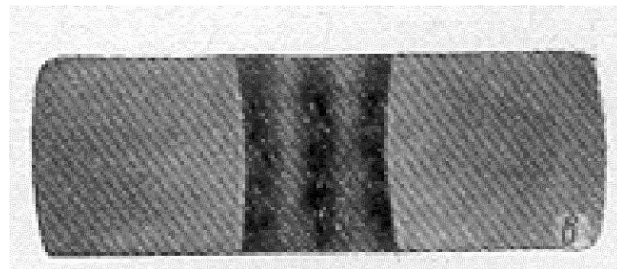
б – Формозміна товстостінної кільцевої заготовки
